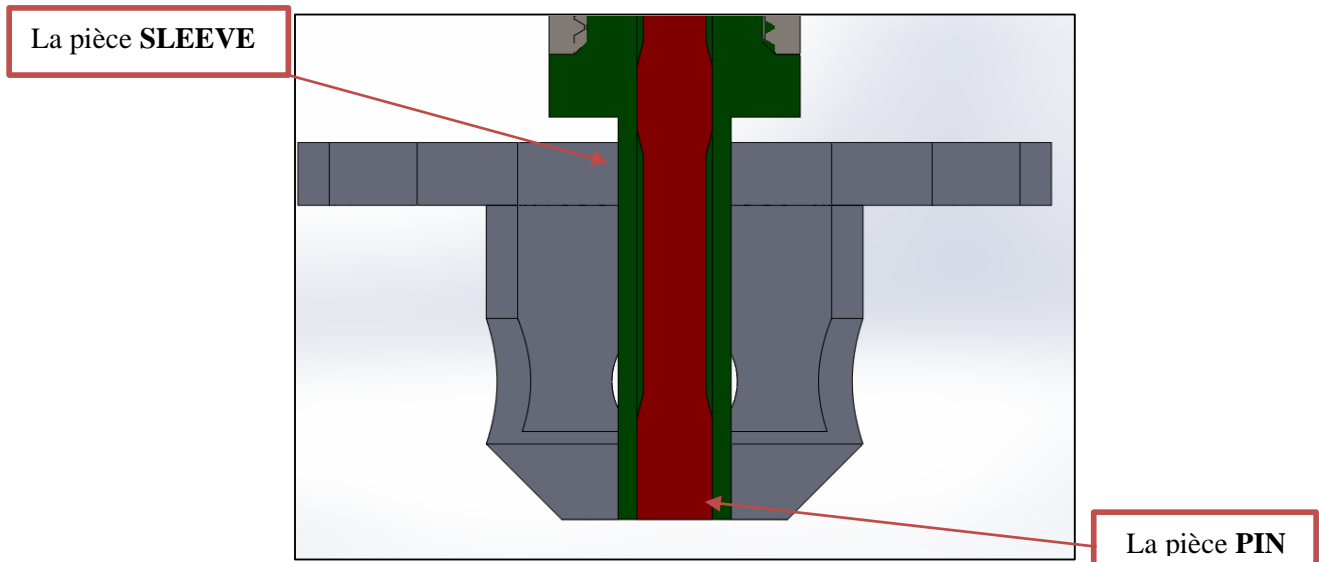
vue de coupe de l'alignement du clamping ring avec le sleeve.
